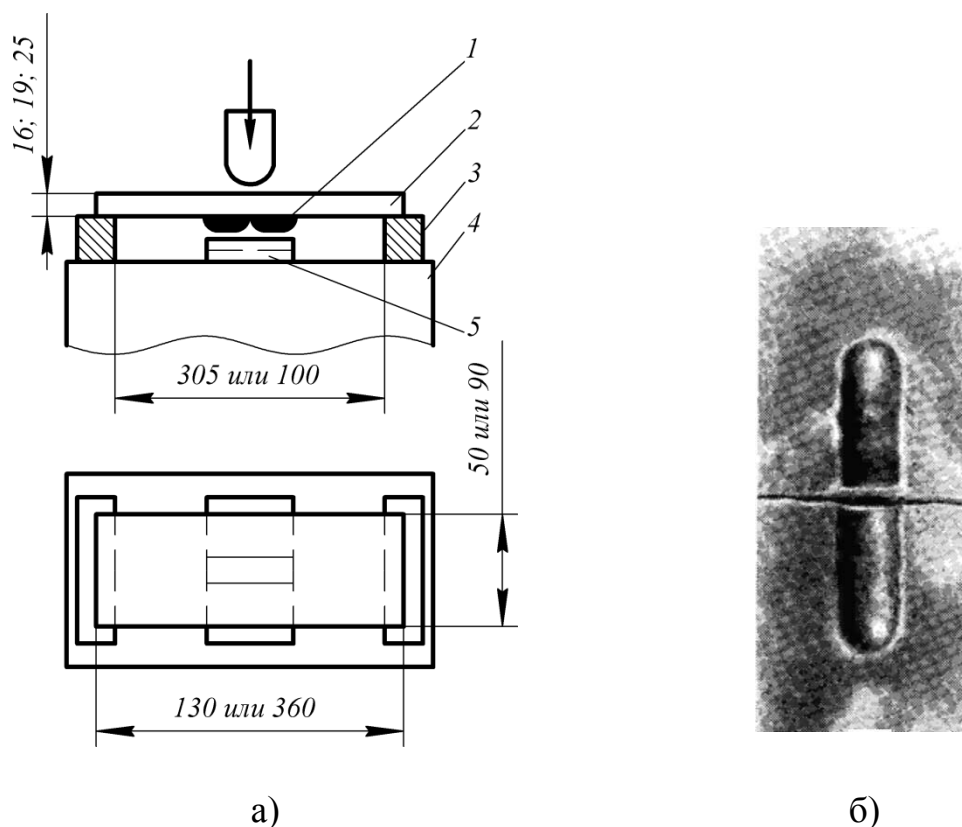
Испытание падающим грузом: а – схема проведения испытаний; 1 – наплавленный валик с надрезом; 2 – образец; 3 – опора; 4 – плита; 5 – ограничитель; б – образец судостроительной стали после разрушения
